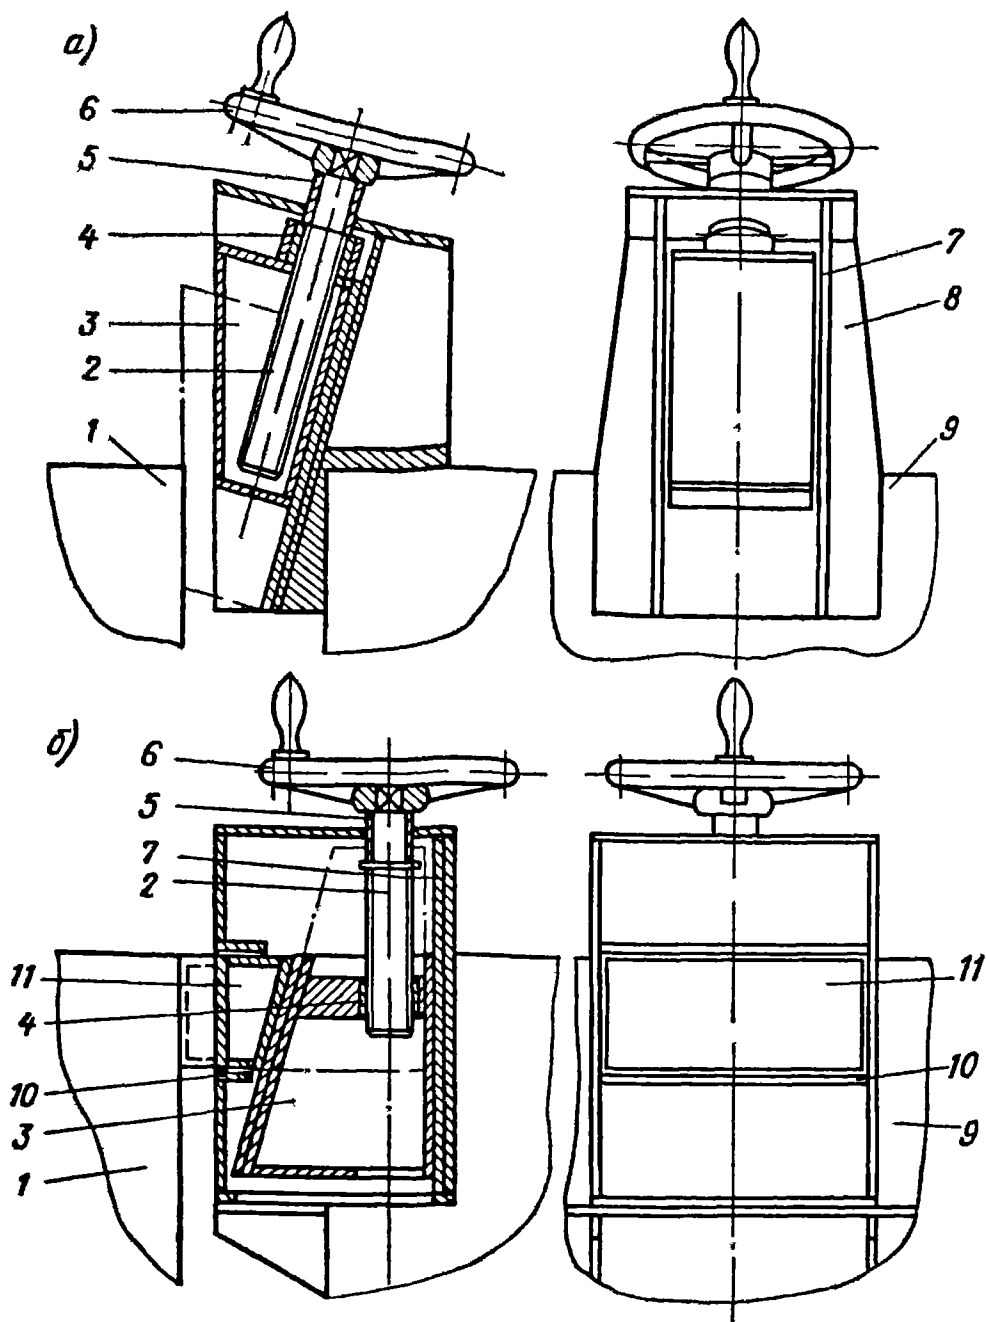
Схемы креплений лихтеров в трюме: а — клинового типа; б — упорно-клинового типа.
